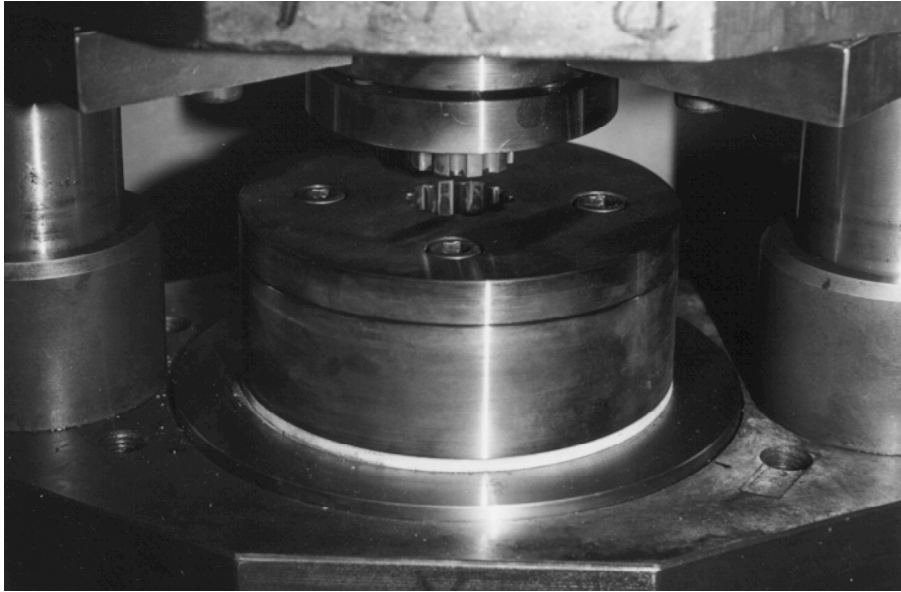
Werkzeugsystem mit Säulenführungsgestell zum Präzisionsschmieden der Laufrolle
